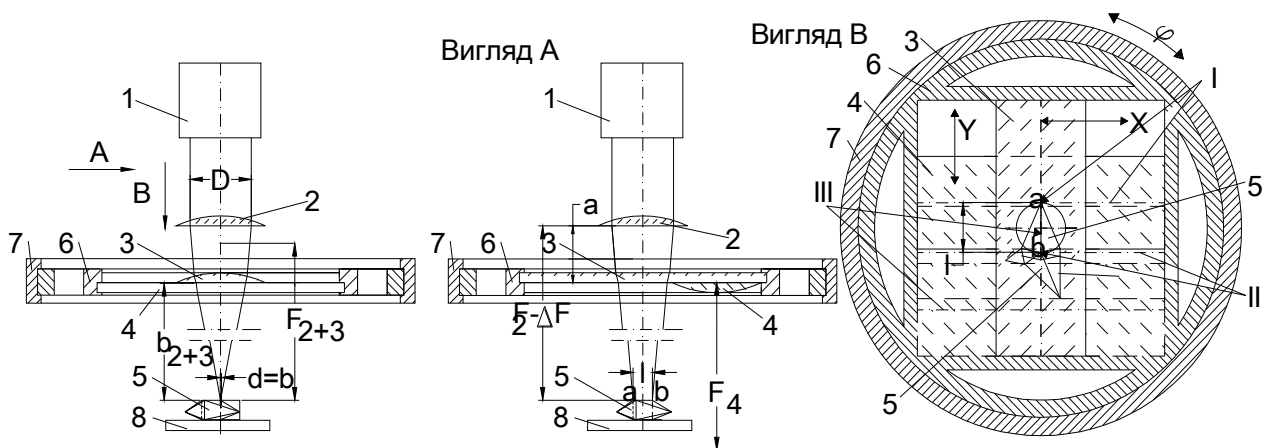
Схема пристрою для комплексної лазерної обробки кристалів: 1 – лазер, 2 – лінза сферична, 3, 4 – лінзи циліндричні, 5 – кристал, що обробляється, 6 – оправка, 7 – корпус системи циліндричних лінз
